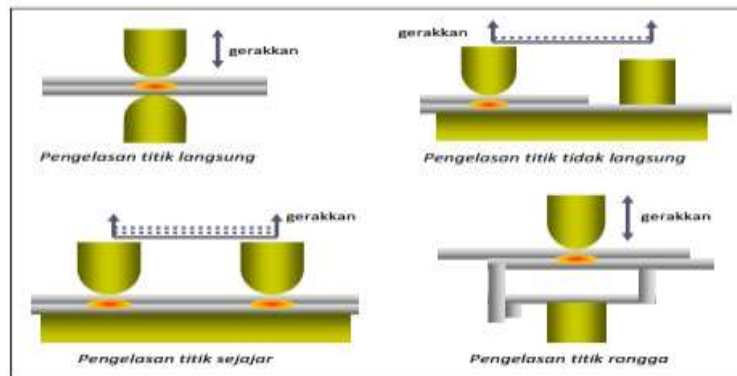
Rangkaian *Spot Welding
